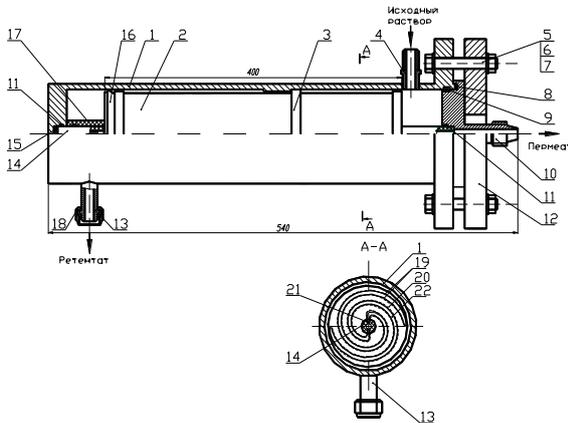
Схема обратноосмотического рулонного модуля: 1 – корпус; 2 – рулонный элемент; 3 – резиновая манжета; 4 – штуцер ввода исходного раствора; 5, 6, 7 – болт, гайка и шайба; 8 – прокладка; 9 – резиновое кольцо; 10 – крышка; 11 – резиновое кольцо; 12 – фланец; 13 – штуцер вывода ретентата; 14 – трубка для отвода пермеата; 15 – заглушка; 16 – решетка; 17 – втулка; 18 – накидная гайка; 19 – мембраны; 20 – сетка-сепаратор (турбулизатор); 21 – отверстия отвода пермеата; 22 – дренажный слой
